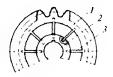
Шлифовальный шевер е плоскими рессорами:
